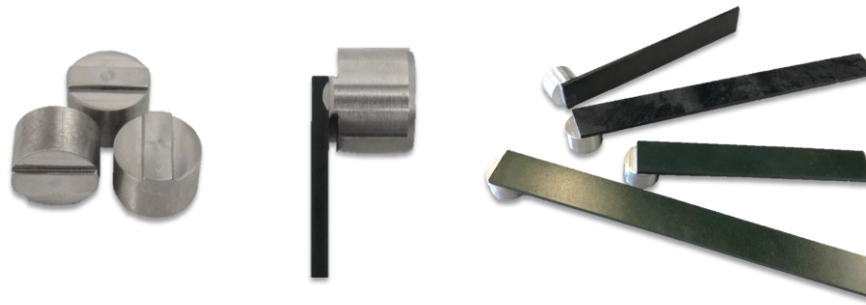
Links: Probenadapter, Mitte: Klebung, Rechts: Probekörper mit Probenadapter [UM20]
